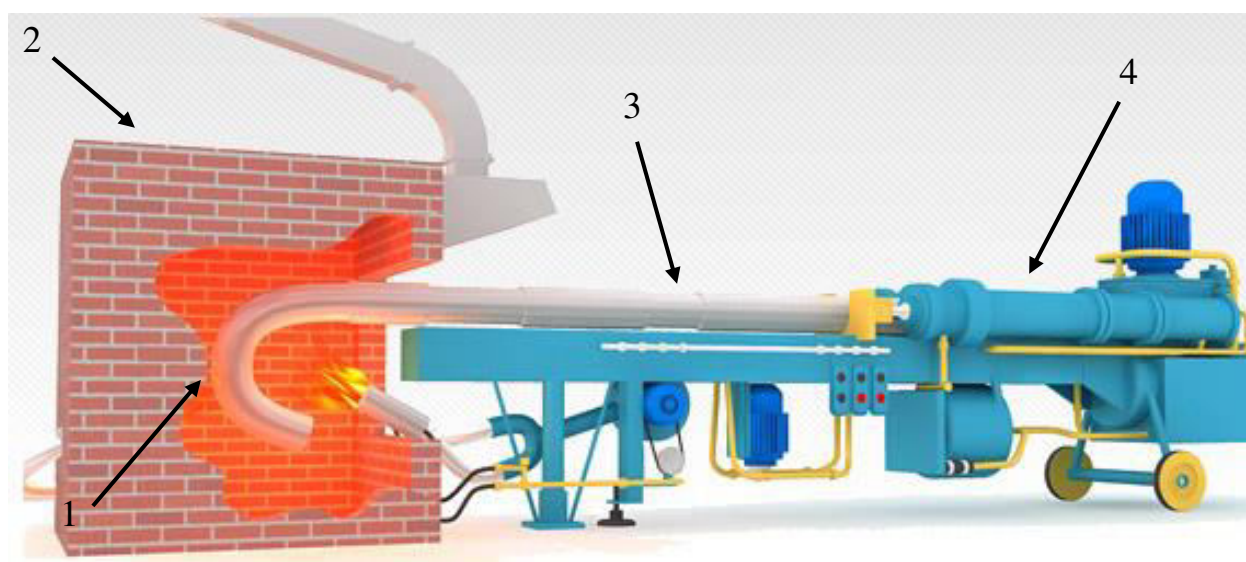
Процесс протяжки трубы-заготовки через рогообразный сердечник;
